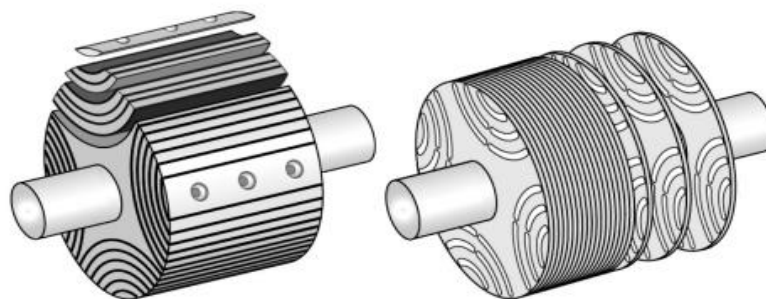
Základní rozdělení synchronních reluktančních motorů podle typu rotoru.
